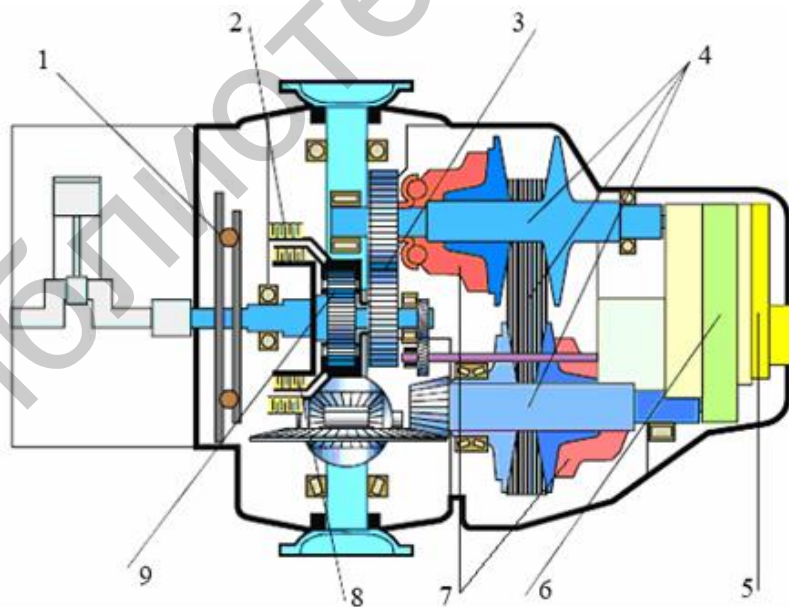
Схема бесступенчатой коробки передач автомобиля Audi:
